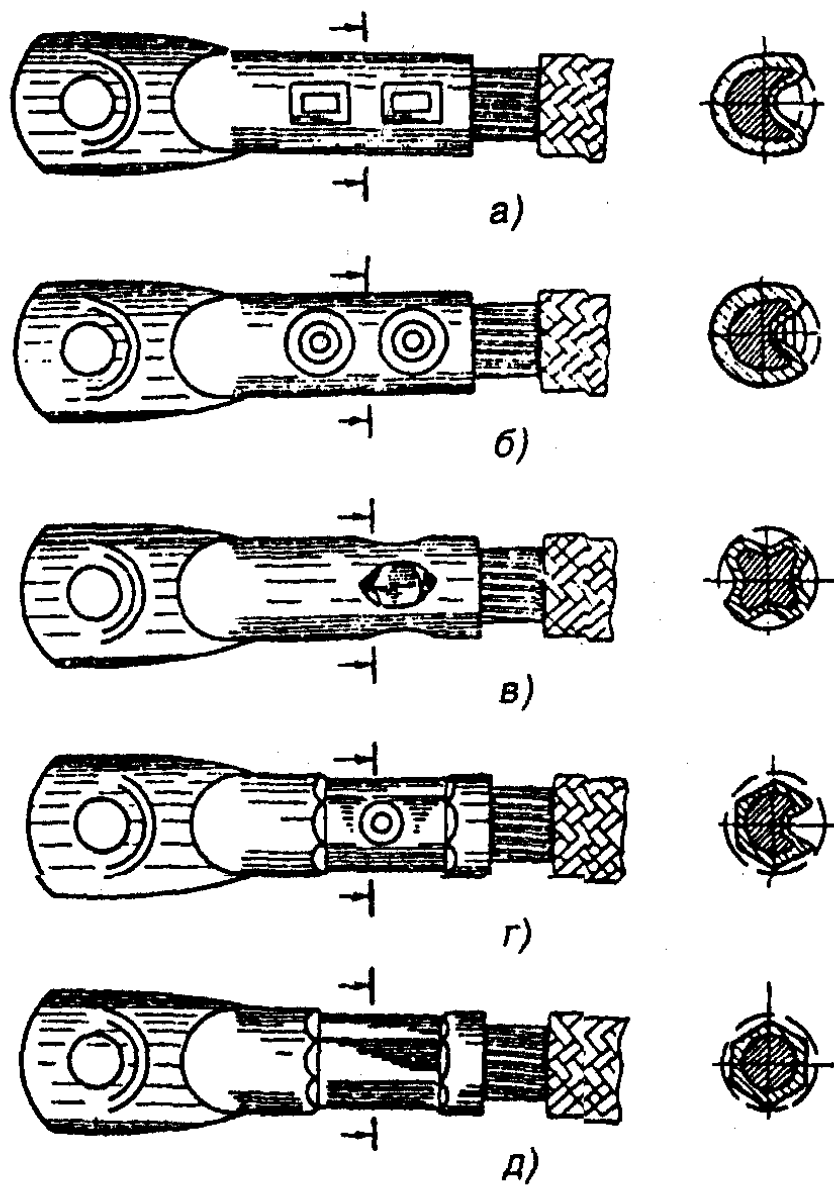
Общий вид контактных соединений, выполненных различными способами опрессовки:
